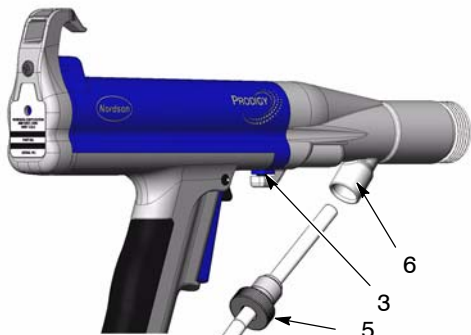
Odłączanie korpusu pistoletu od rękojeści
